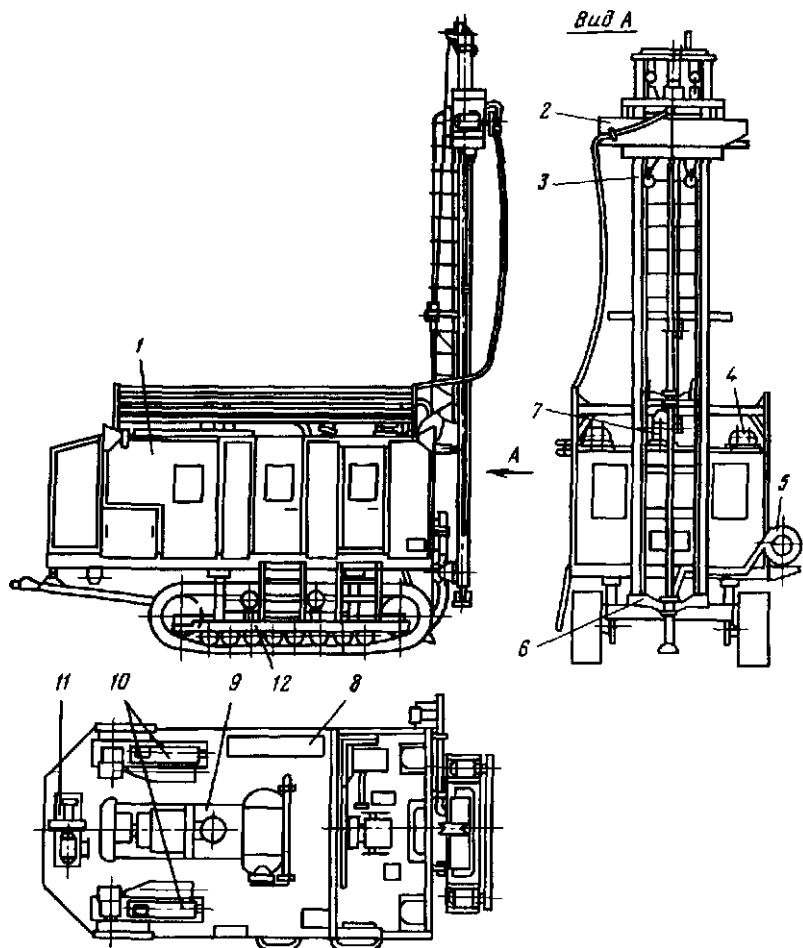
Общий вид станка вибровращательного бурения СВВ-42 для установки гидронгл:
